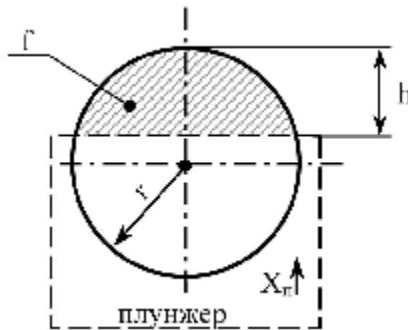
Схема открытия (закрытия) круглого окна втулки ТНВД
